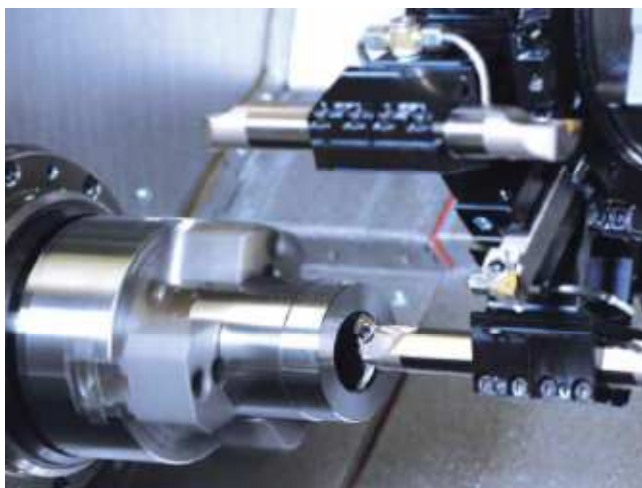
Pracovní prostor univerzální soustruh SV 18 R [2]
